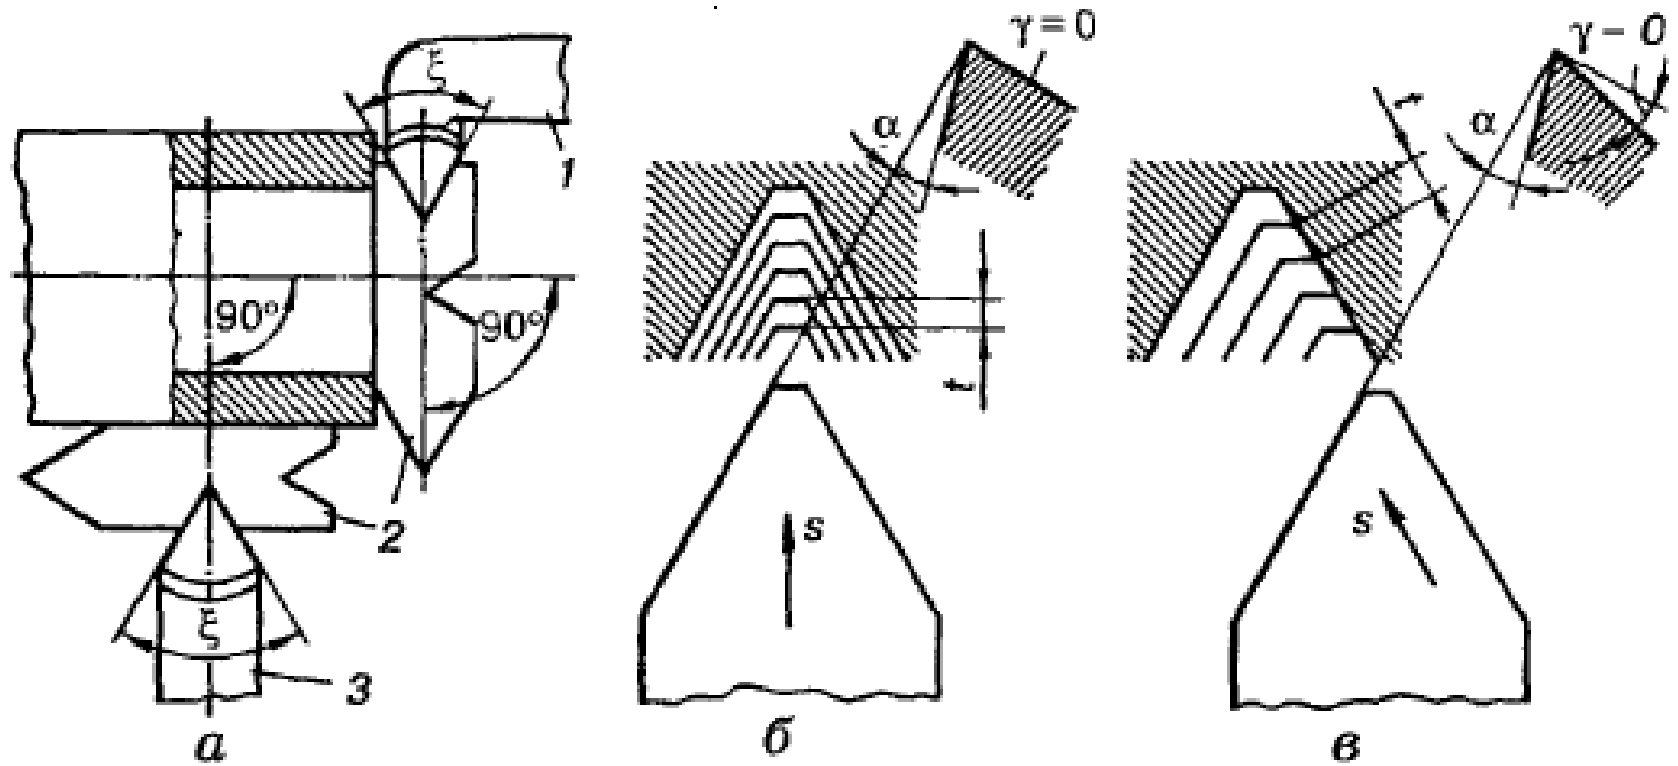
Схеми нарізання різьби різцями на токарному верстаті
